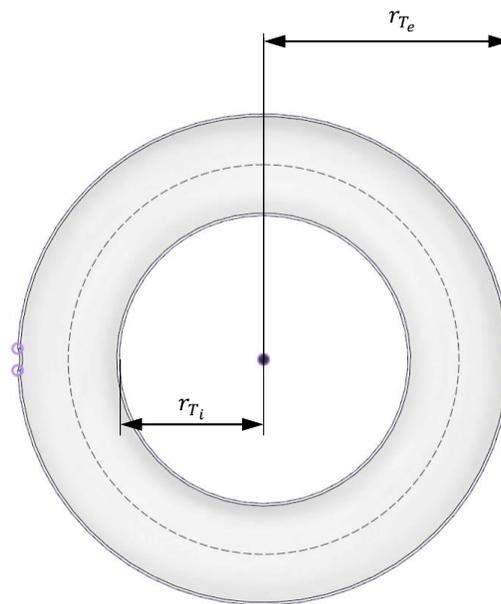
Vista in sezione dall'alto della geometria toroidale.
